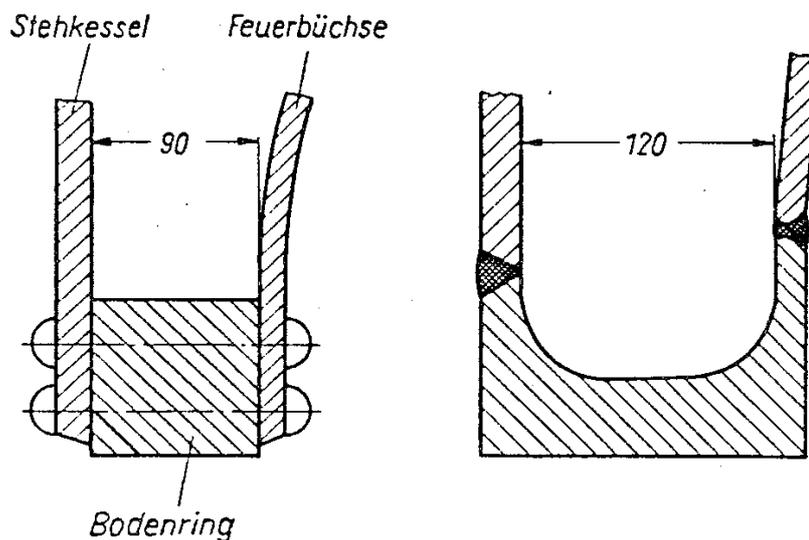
Bodenring am genieteten und geschweißten Kessel
